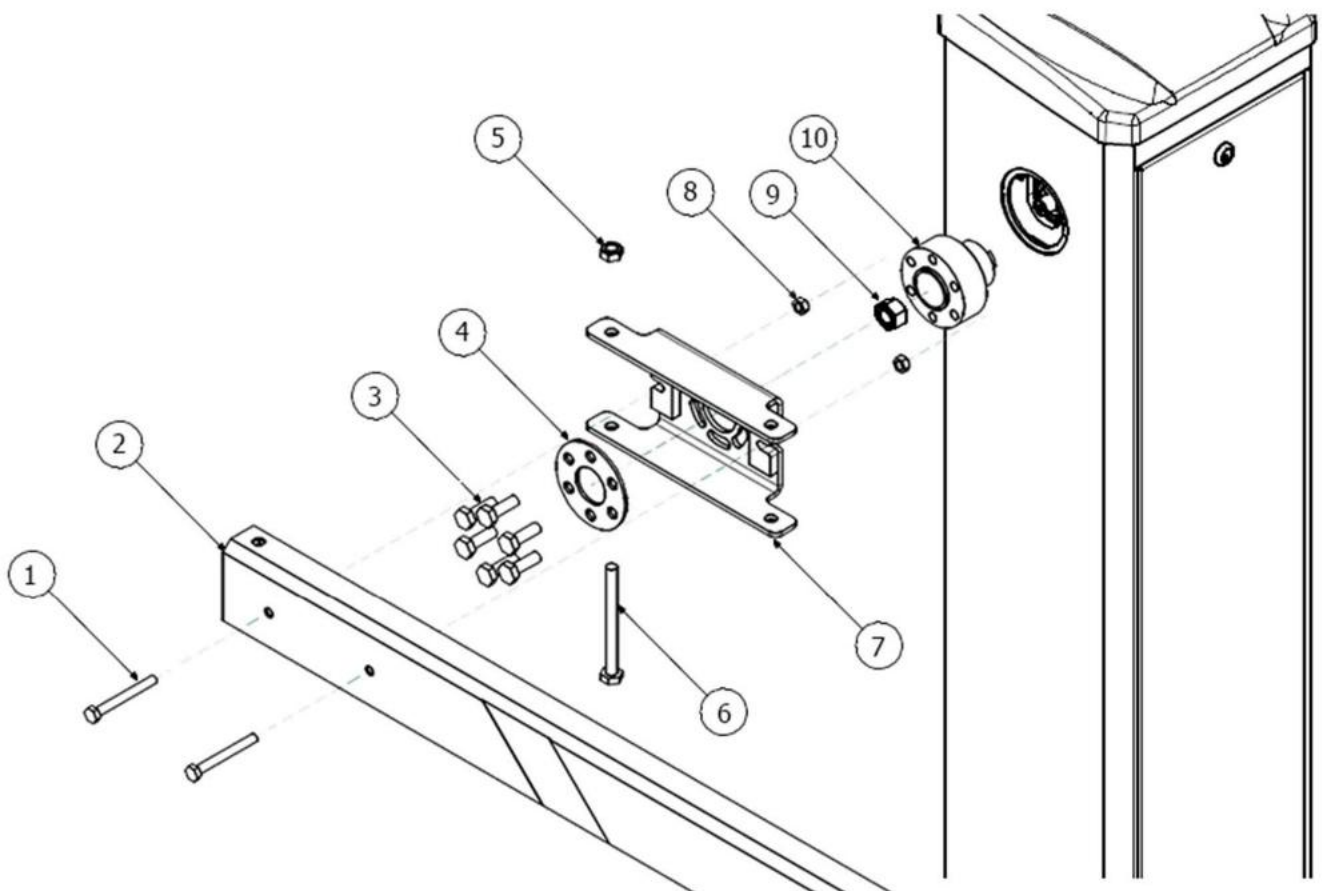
Entfernen der Schrankenarm-Klemmenbaugruppe
